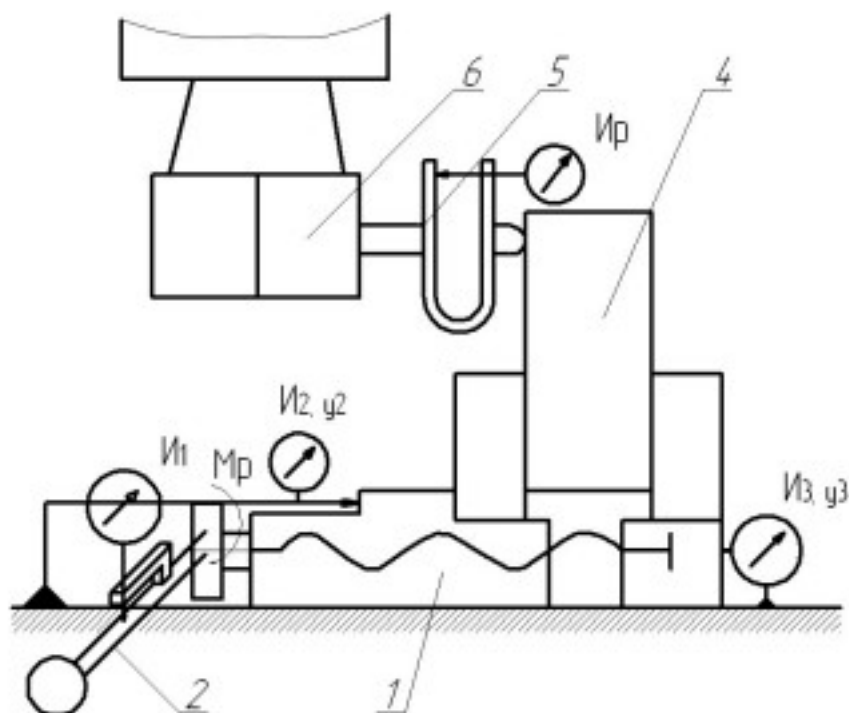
Схема заміру податливості лещат при навантаженні на нерухому губку: 1- машинні лещата; 2- динамометричний ключ; 3- навантажувальний пристрій; 4- заготовка; 5- динамометр камертонного типу; 6- шпиндель фрезерного станка; I1- індикатор з шкалою 0.01мм; I2- індикатор з шкалою 0.01мм; I3- індикатор з шкалою 0.01мм; Iр- індикатор з шкалою 0.01мм
